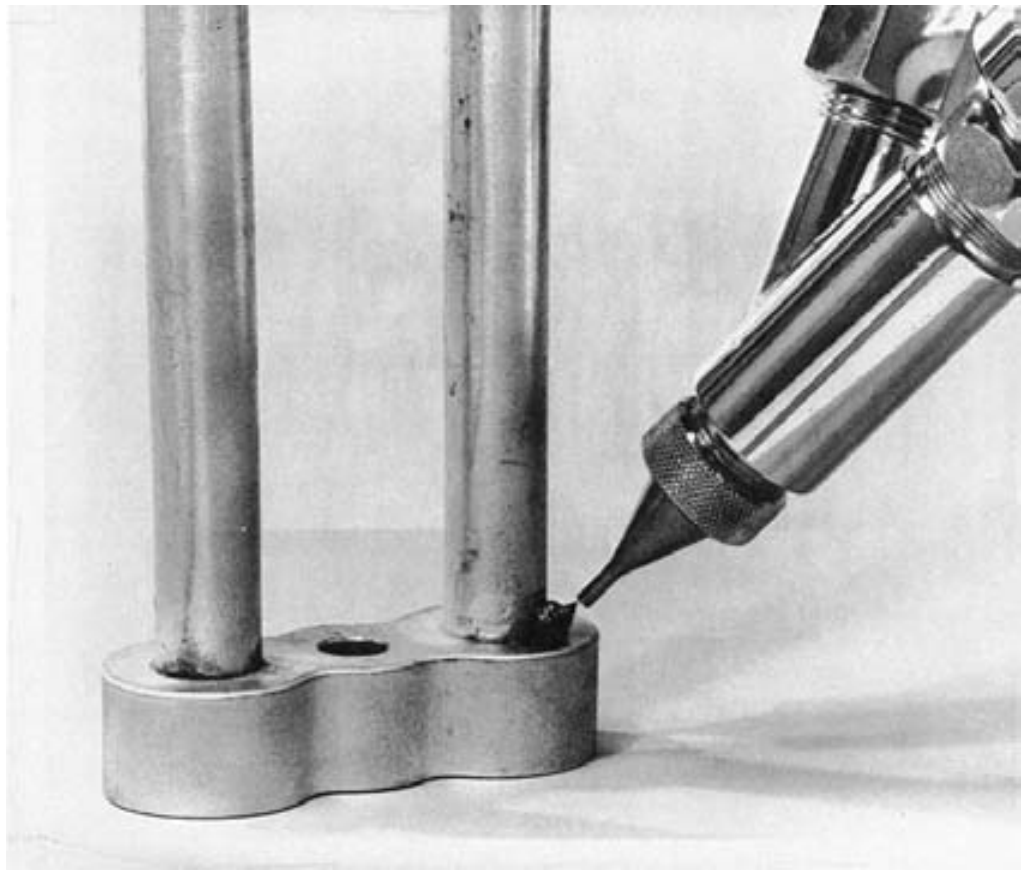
Aplicación de pasta para soldadura dura a una unión mediante dispensador. (Foto cortesía de Fusion, Inc.).
